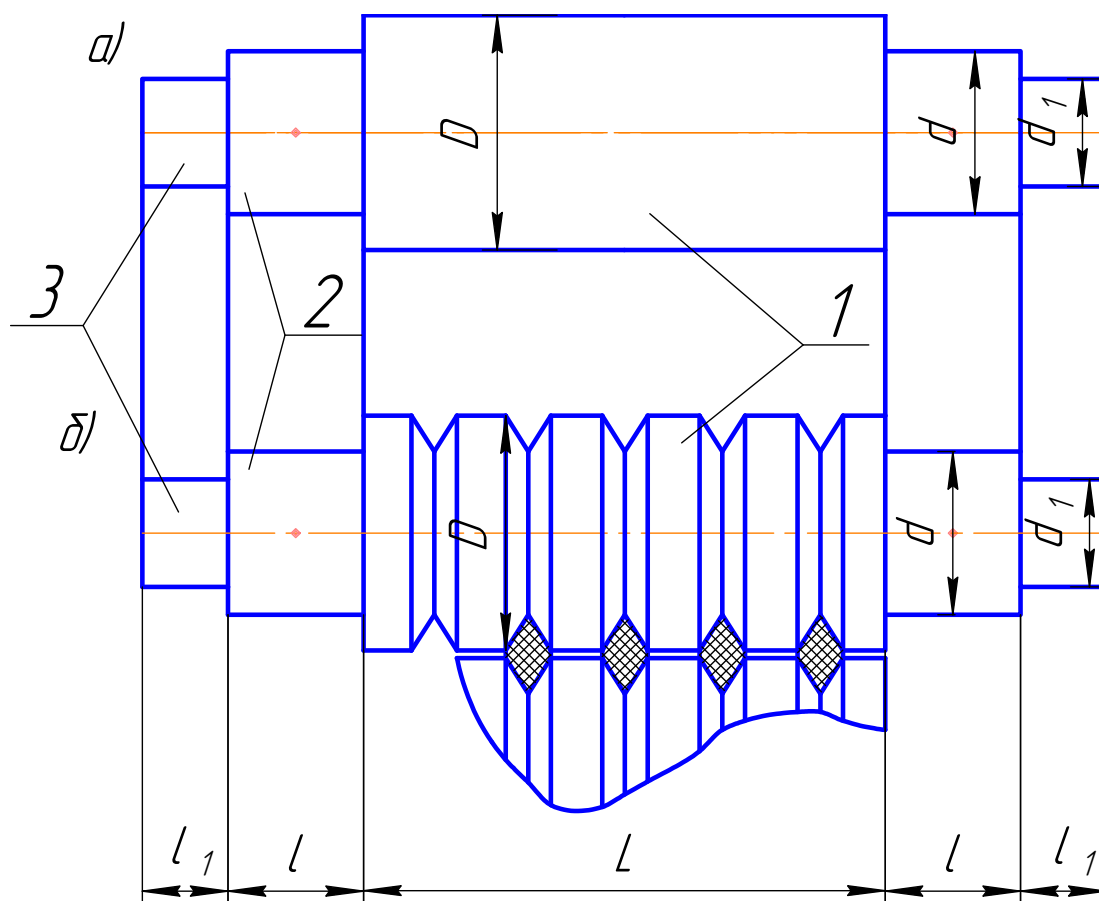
Схеми розташування валків у робочих клітках:
